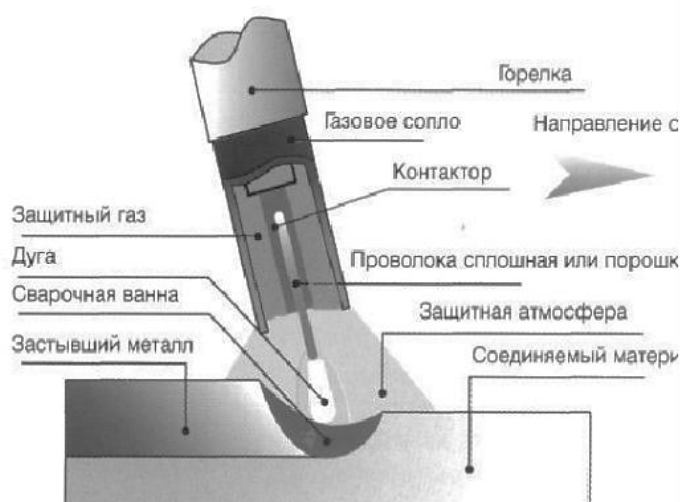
Схема ручной дуговой сварки в среде защитных газов
